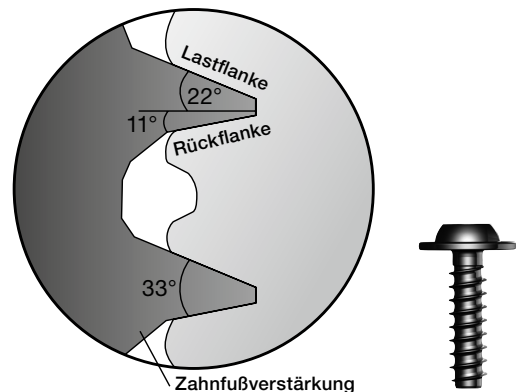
Direktverschraubung mit einer ALtracs® Schraube in Leichtmetall
